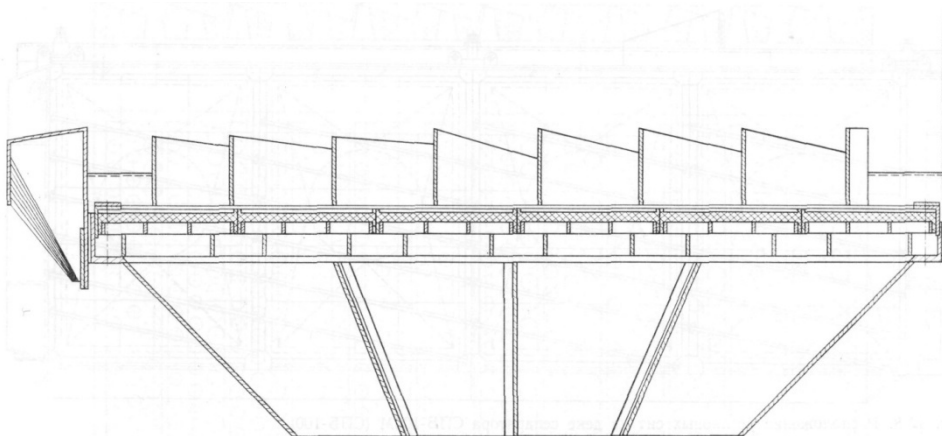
Поперечный разрез рабочего короба сепаратора ОСП-100 с резиновыми ситами
